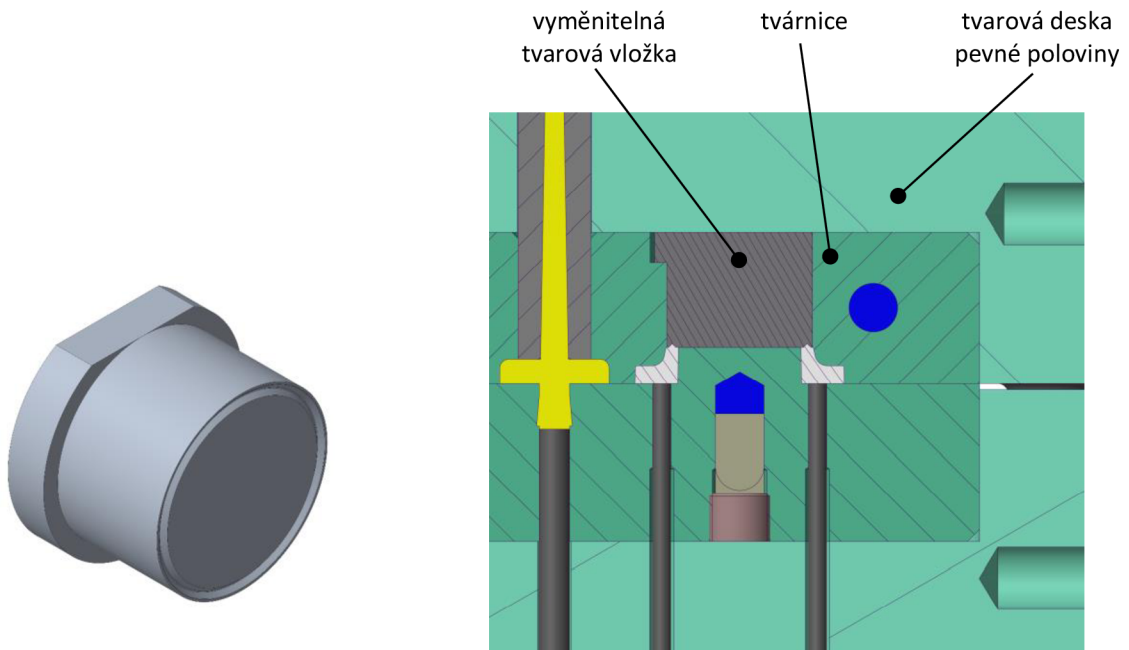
Rozmístění vyhazovacích kolíků – varianta b)
